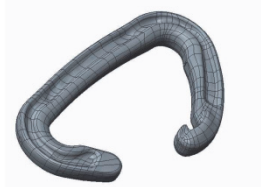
Mittels 3D-Scanner generiertes 3D-Modell [3].
